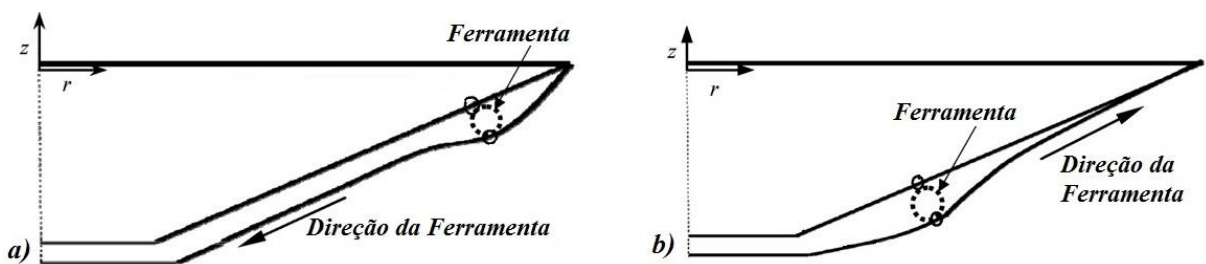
Representação esquemática da estratégia de estampagem: a) “out-to-in”; b) “in-to-out” [33]
